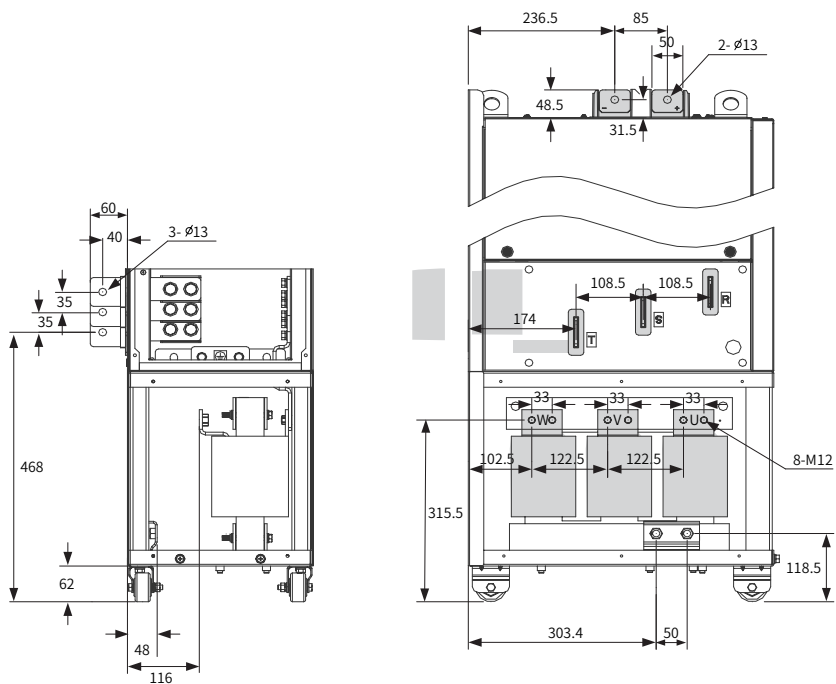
Размеры клемм главной цепи MD880-01S-0441-4(-L)/MD880-01S-0481-4(-L) (с выходными реакторами)
